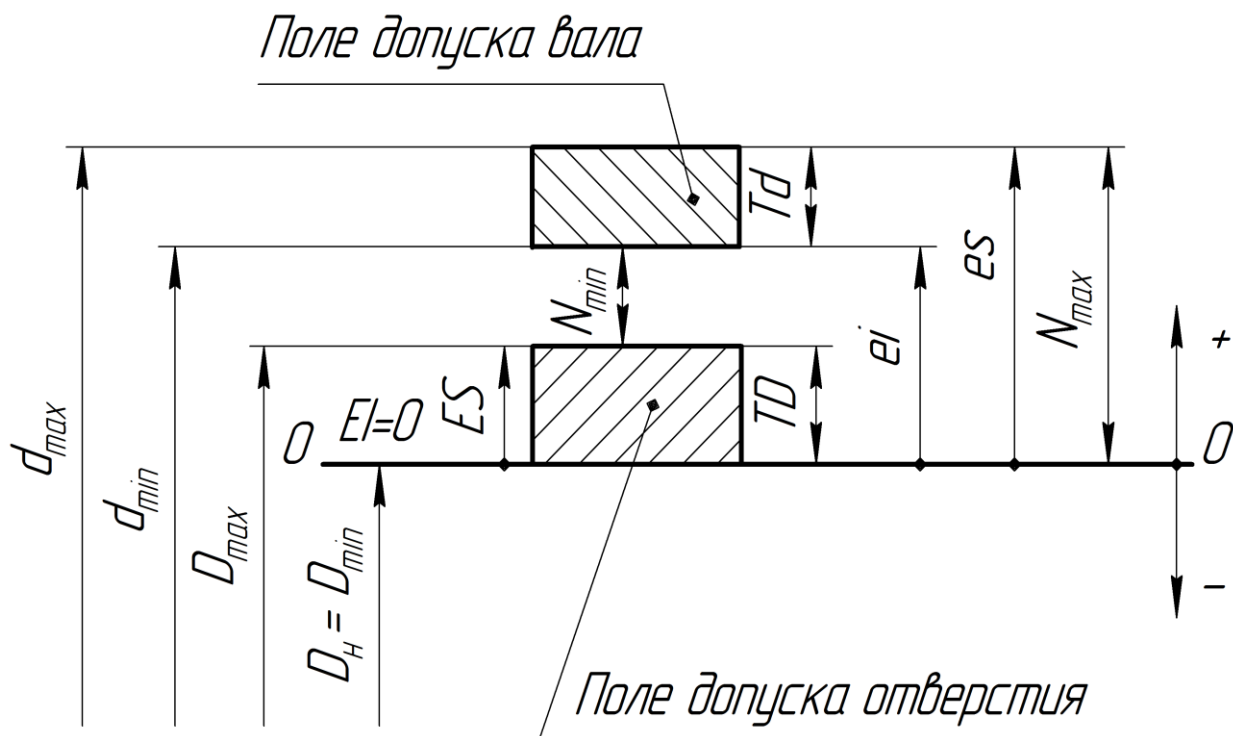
Схема расположения полей допусков в посадке с натягом
